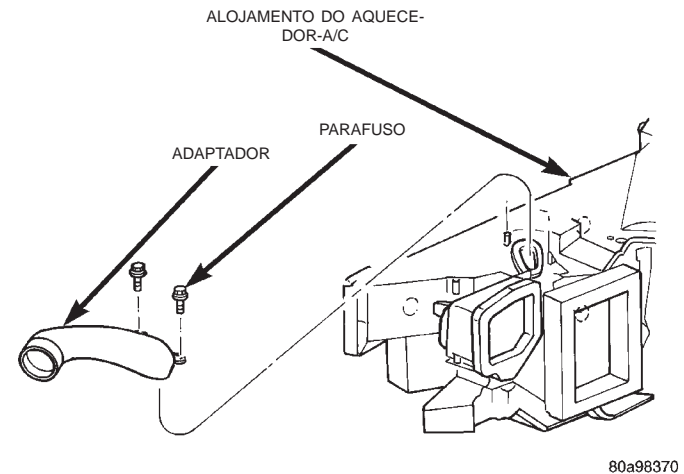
Remoção/Instalação do Adaptador do Duto do Desembaçador
